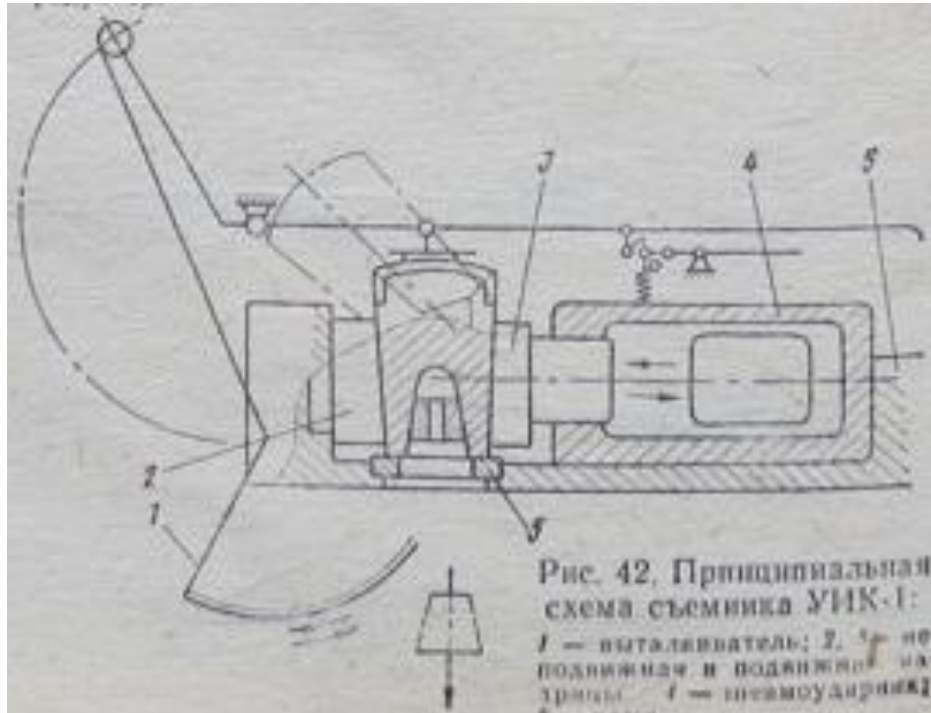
Схема пневматичного знімача УІК-1:
